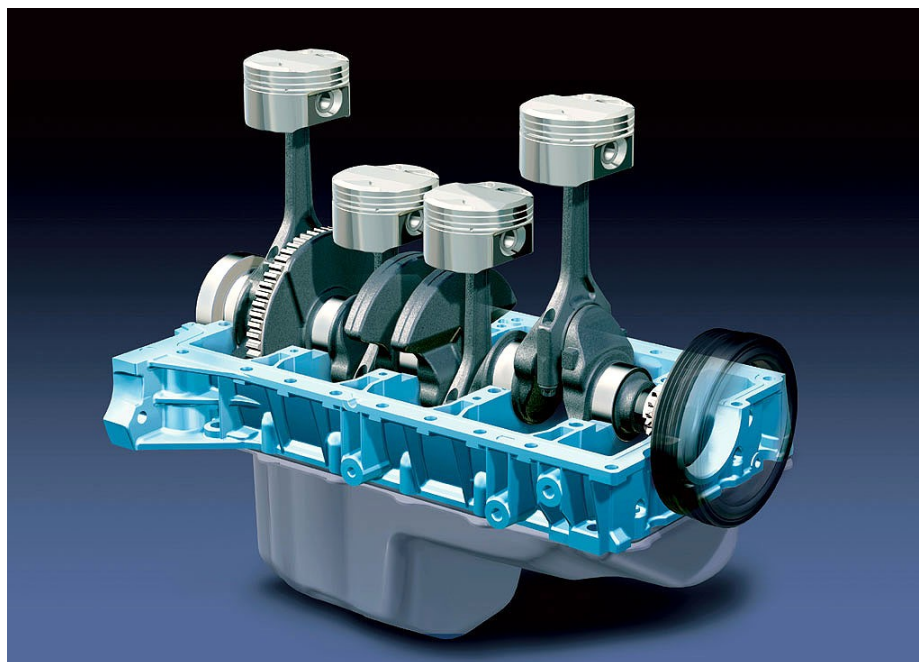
Imagen del Cigüeñal montado sobre el Carter
